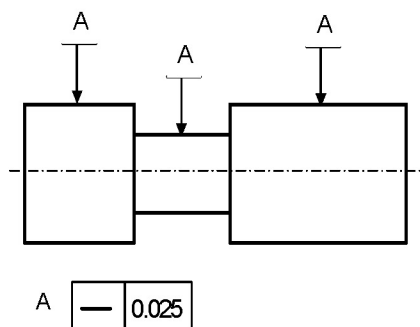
Tolerancia geométrica con línea de referencia interrumpida
